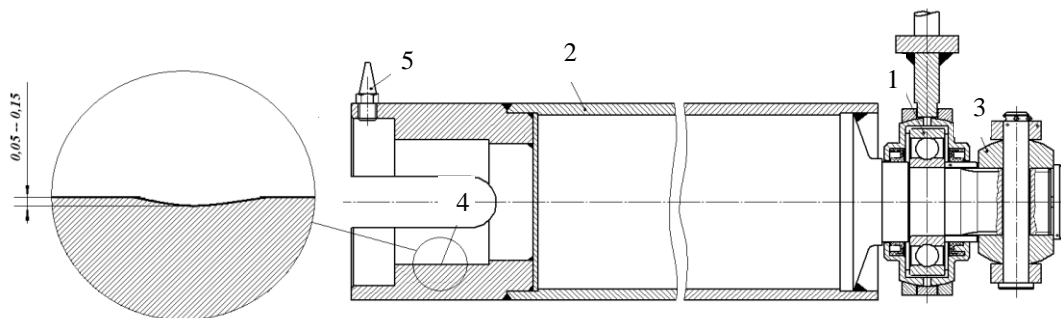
Схема расположения износа на контактной поверхности муфты:
